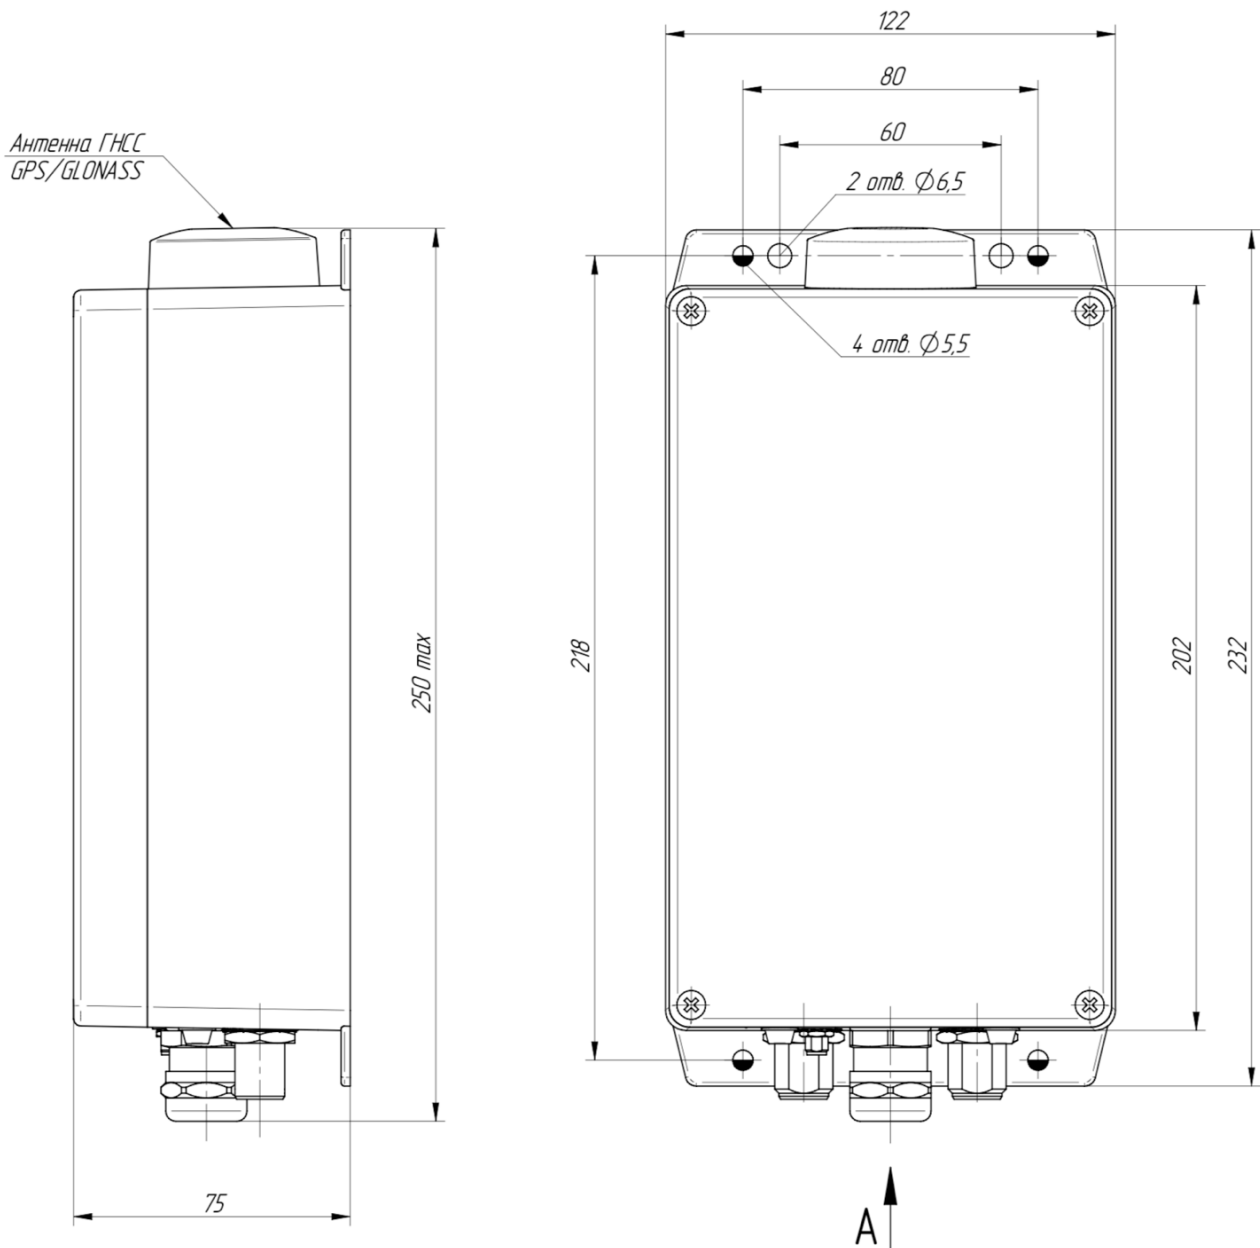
Габаритные размеры приемо-передающего блока базовой станции
